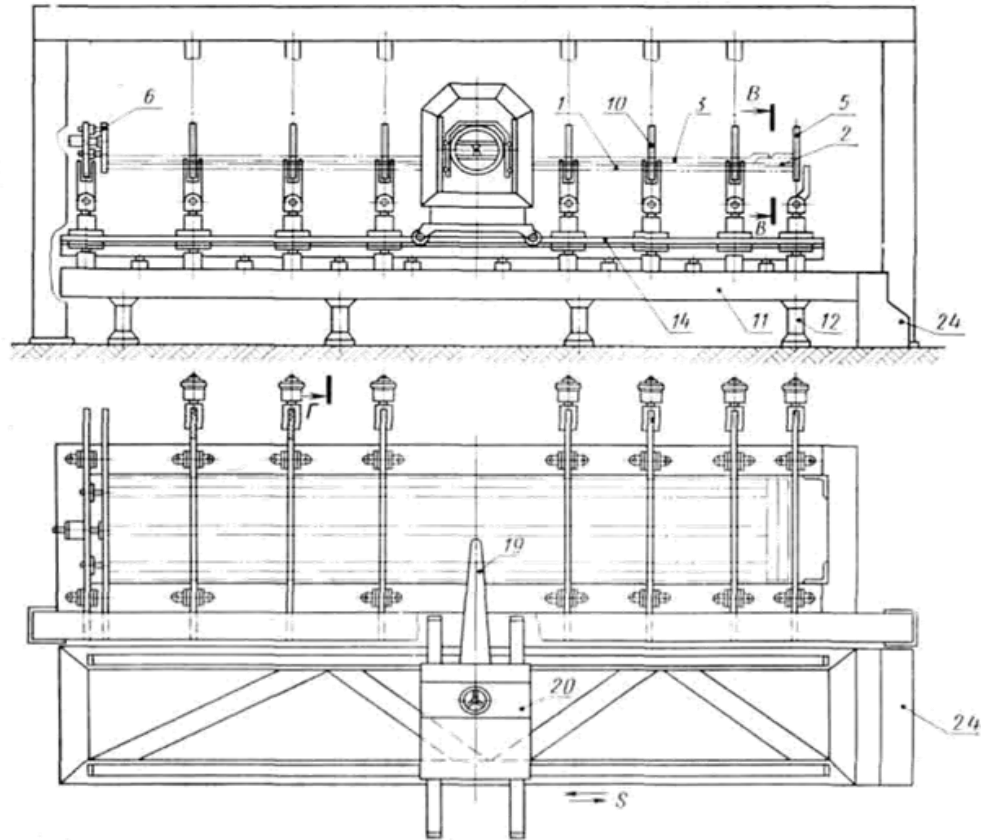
Компоночный чертеж сборки и сварки панели
